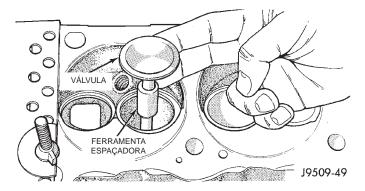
Posicionamento da Válvula com a Ferramenta C-3973
